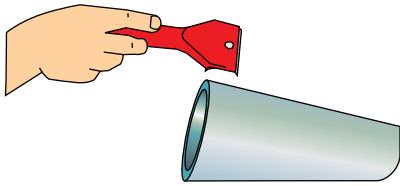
Перед початком процесу зварювання необхідно зіскоблювати з поверхні труби оксидний шар.
